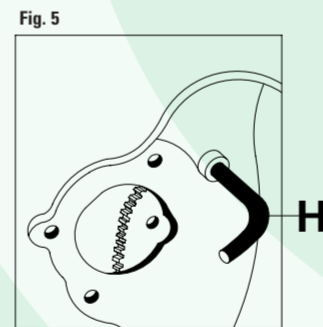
Insertar la herramienta de inmovilización del volante motor H.
